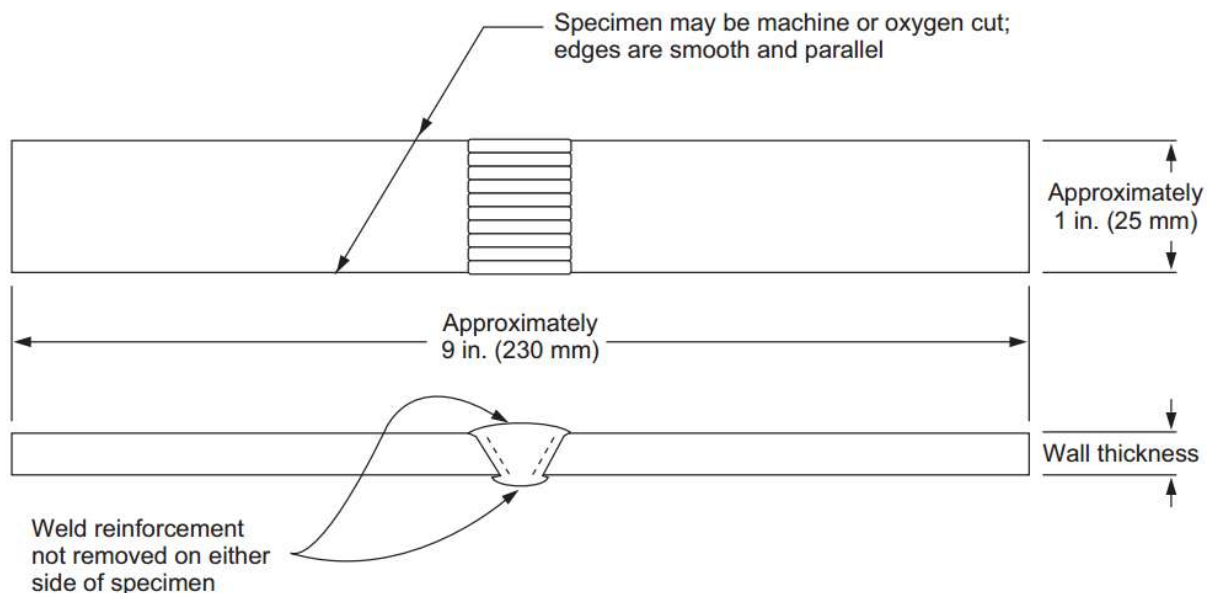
Dimension de l'éprouvette de traction [33].
